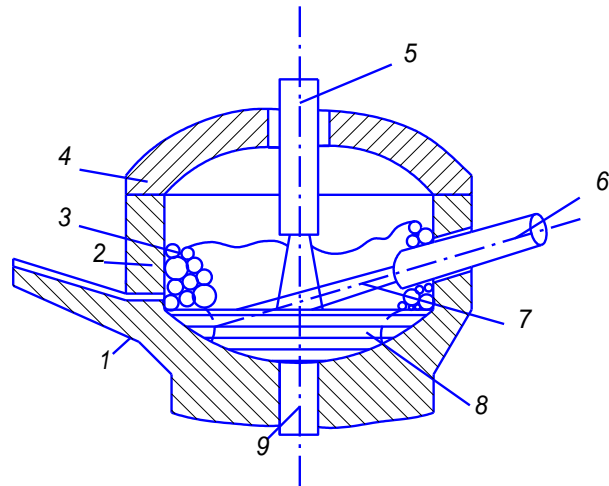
Плазменно-дуговая сталеплавильная печь постоянного тока: 1 – кожух; 2 – футеровка; 3 – шихта; 4 – свод; 5 – сводовый плазматрон; 6 – стеновой плазматрон; 7 – дуга; 8 – ванна металла; 9 – подовый электрод
